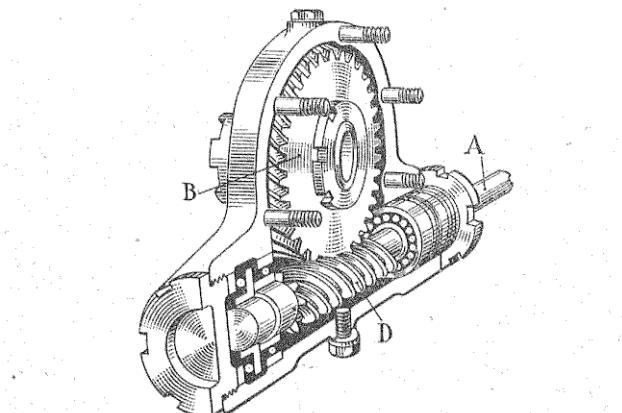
Commande du moyeu arrière par vis sans fin.
